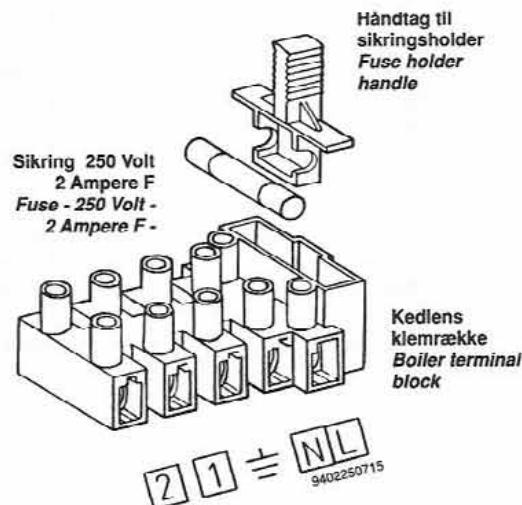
Udskift sikringen ved at trække ud i håndtaget.
